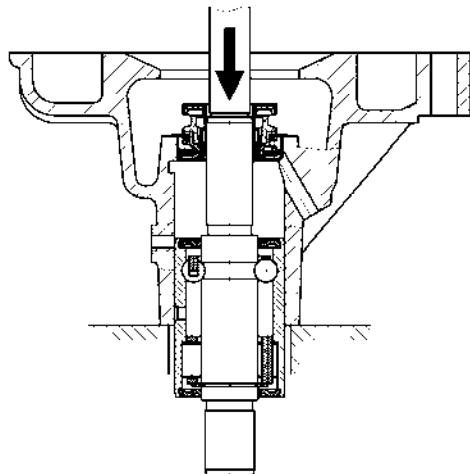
Выпрессовка подшипника с валиком водяного насоса
